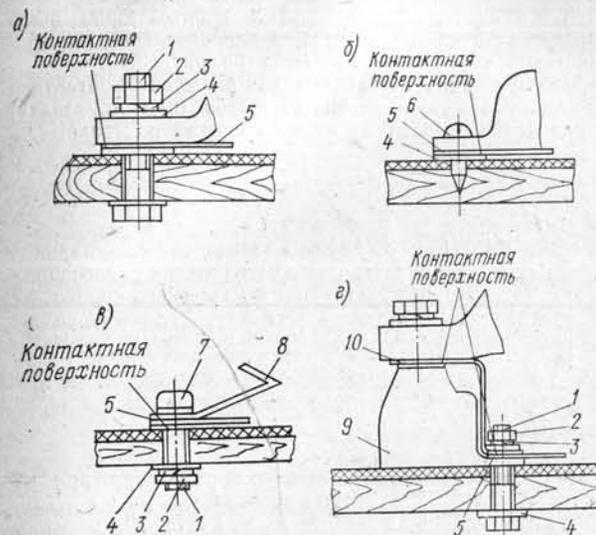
Узлы крепления и заземления корпусов на деревянных основаниях с декоративной обшивкой и без обшивки: а, б — неамортизированных; в — с амортизатором типа АКПО; 2 — с амортизатором типа АКСС-М.
